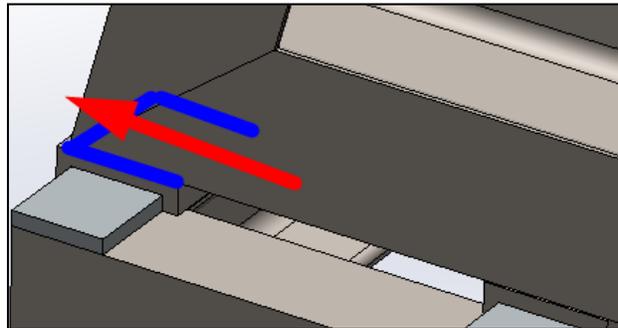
Perfil del cordón de soldadura de la base. Fuente: Elaboración propia.
